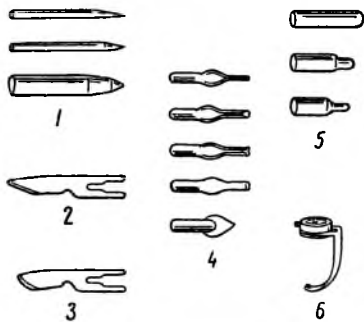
Инструменты и приспособления к электрогравёру: 1 — иглы для гравировки по металлу, стеклу и пластмассам; 2 — нож широкий; 3 — нож узкий толщ. до 2,4 мм; 4 — ножи для художественной резьбы по дереву и пластмассе; 5 — бойки для чеканки по металлу; 6 — подставка для изменения глубины резания ножами
